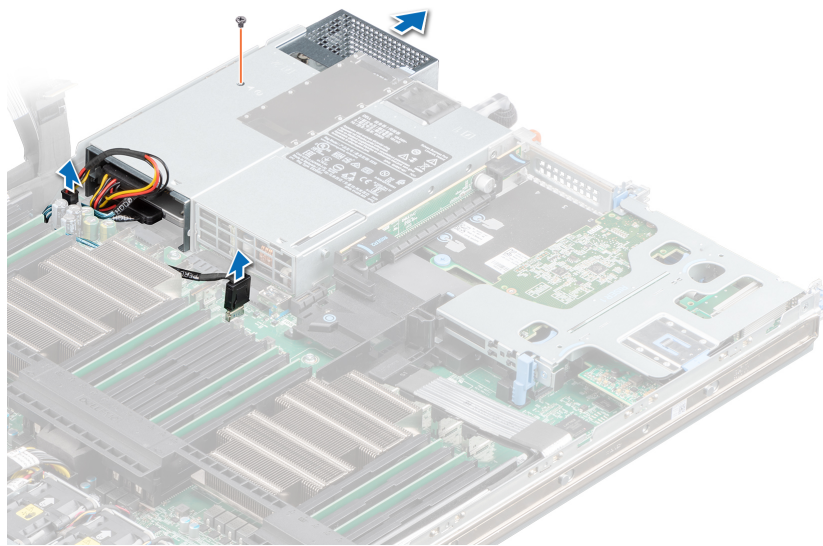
Entfernen des 2,5-Zoll-Laufwerksgehäuses
